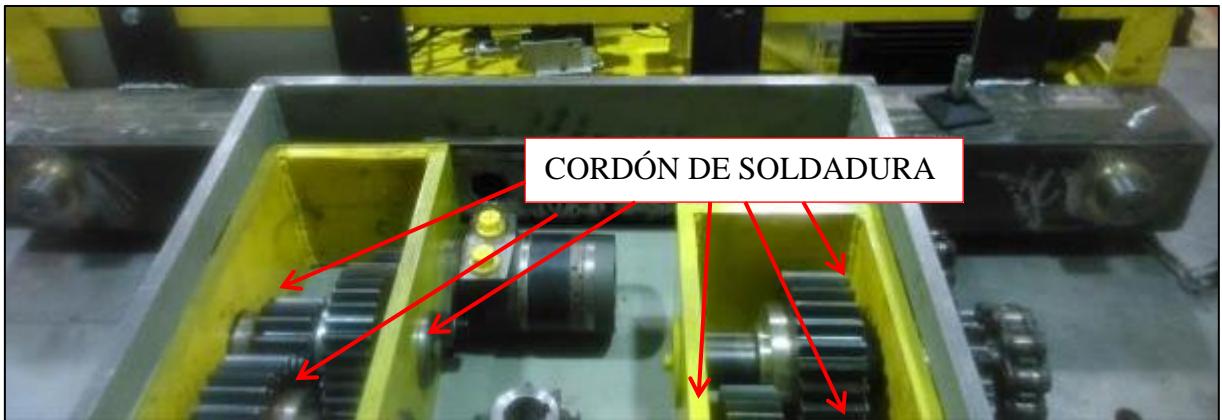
Soldadura ensamblaje caja reductora
